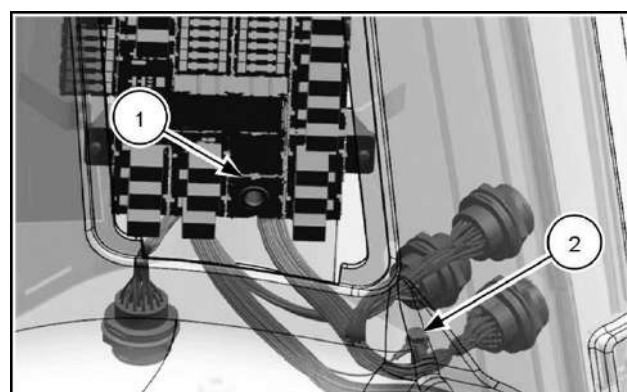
Panel de fusibles, borne de B+ sin conmutar y Masa limpia
